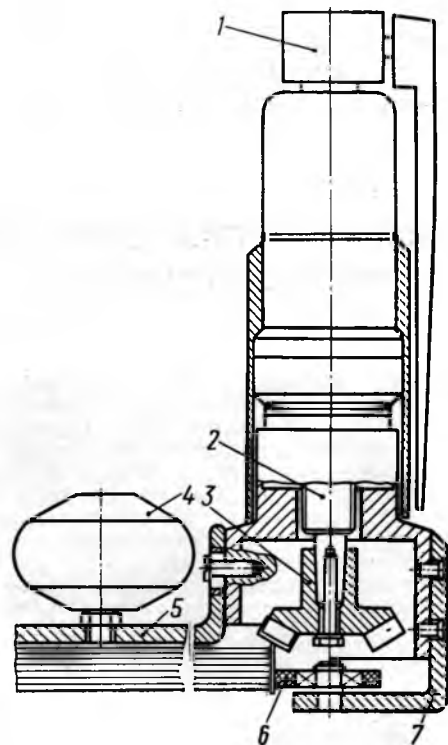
Схема ручной пневматической машинки для снятия свесов кромочного пластика
